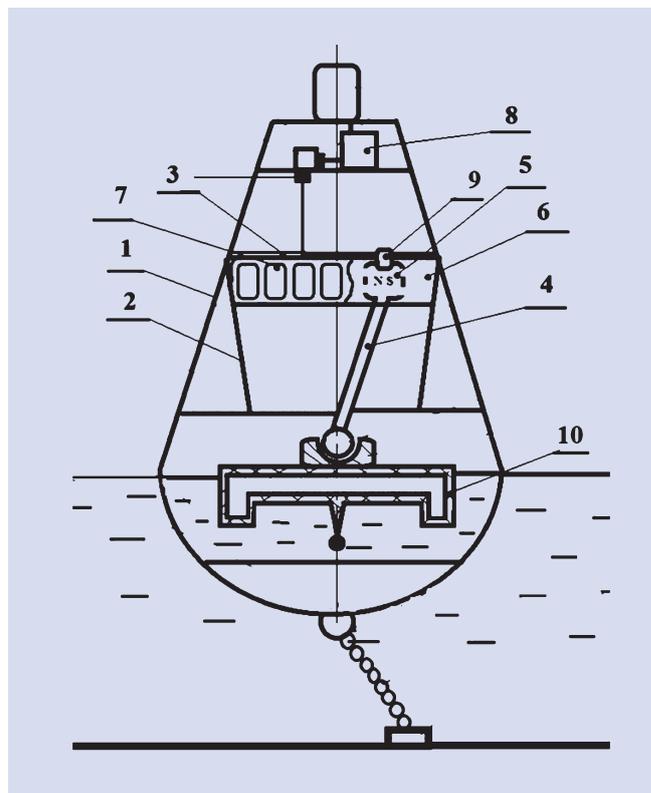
Волноэнергетическая установка: 1 – корпус; 2 – стакан; 3 – направляющая; 4 – стержень; 5 – ротор; 6 – статор; 7 – обмотка статора; 8 – аккумулятор; 9 – захват; 10 – площадка
